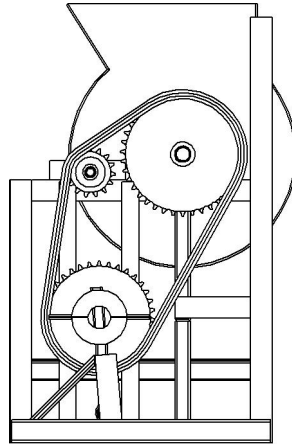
Конструктивна схема розчинозмішувача, вигляд збоку
